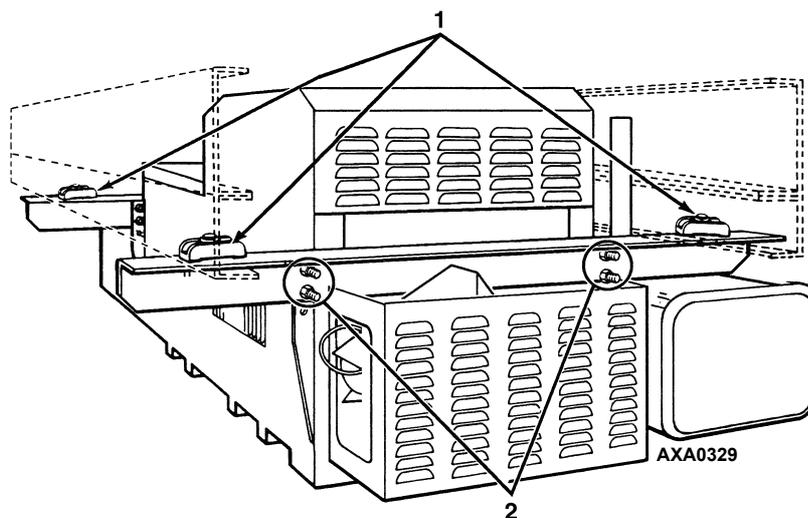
Боковой монтаж SGSM 3000 – заостренный кронштейн
